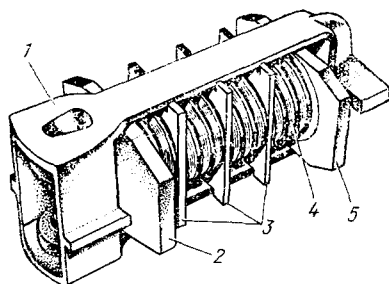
Резино-металлический поглощающий аппарат (бескорпусный):
